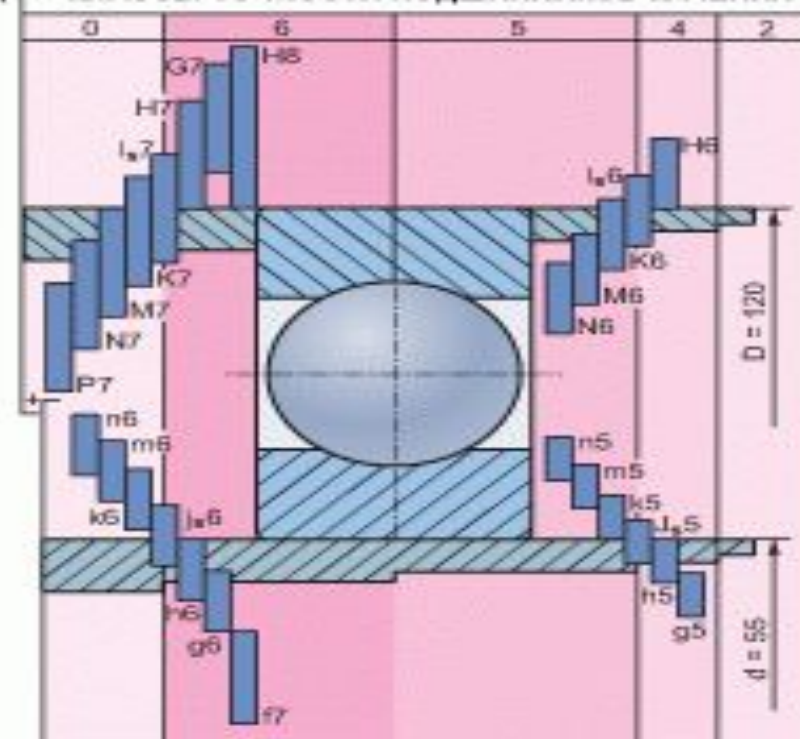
Обозначение посадки внутреннего кольца подшипника на вал
